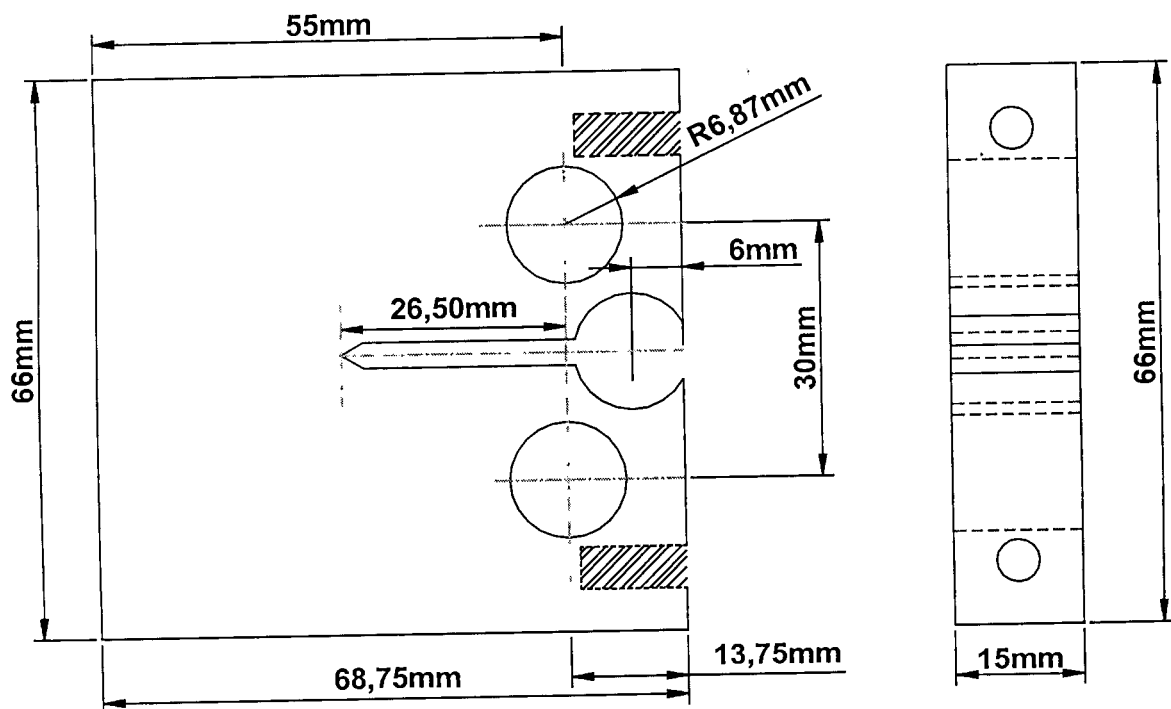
Dibujo del diseño de las probetas de mecánica de fractura (compactas de tensión).
